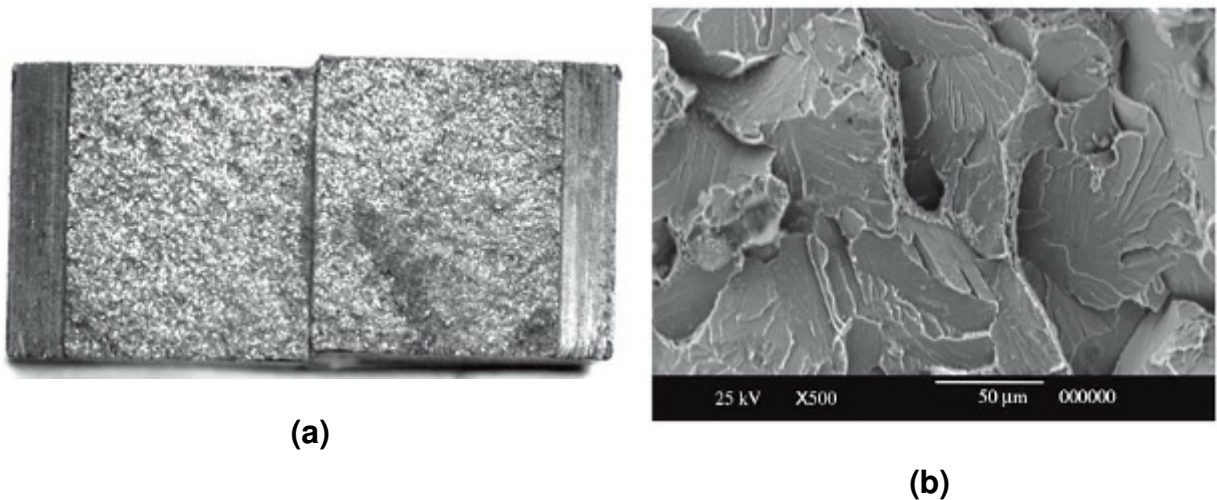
Fractografias representativas de fratura frágil (a) Fractografia de superfície de fratura (b) MEV, magnificação X500
